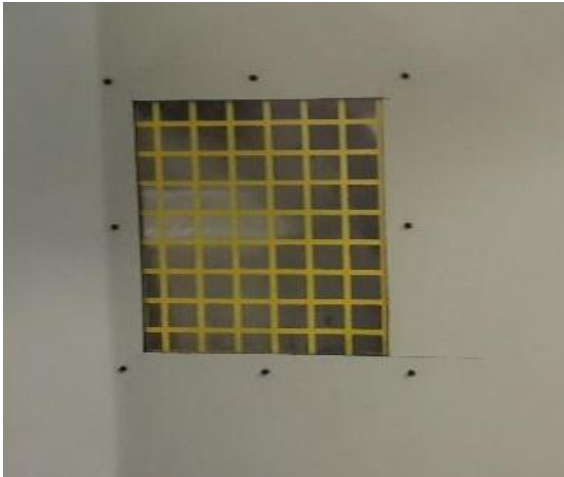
VISOR INSTALADO NA PROTEÇÃO METÁLICA
